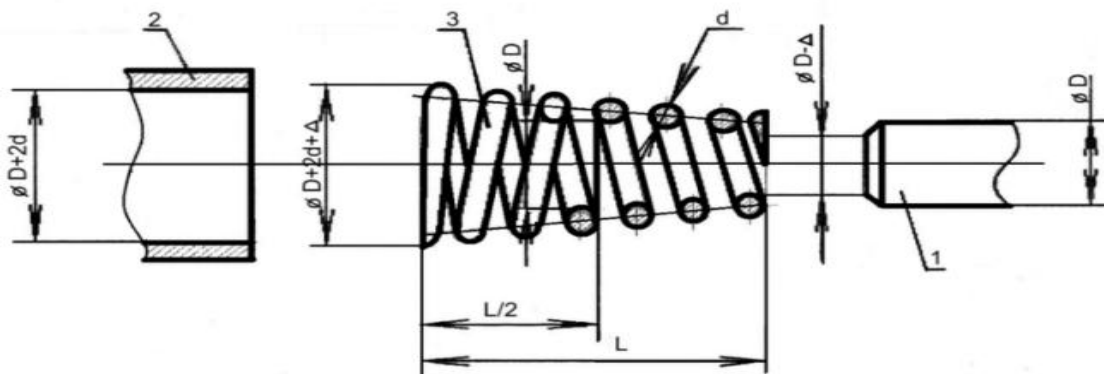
Конический подшипник скольжения для возвратно-вращательного движения
